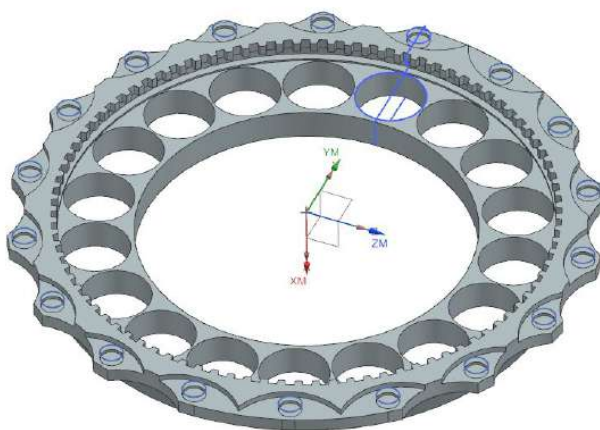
Загальний вигляд базової розрахункової моделі
